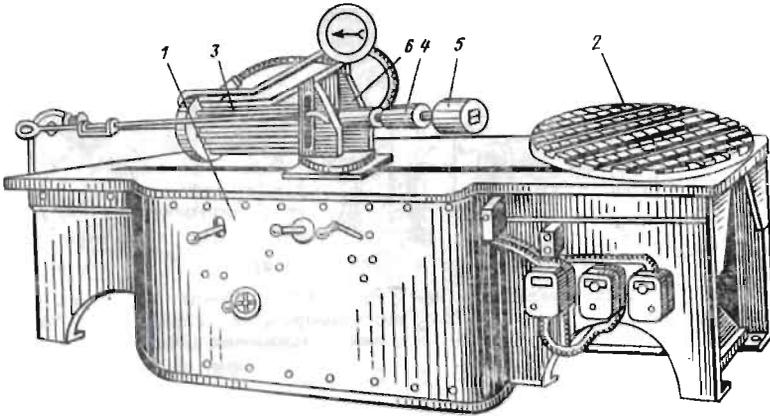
Профилегибочный станок с поворотным столом и растяжным устройством
